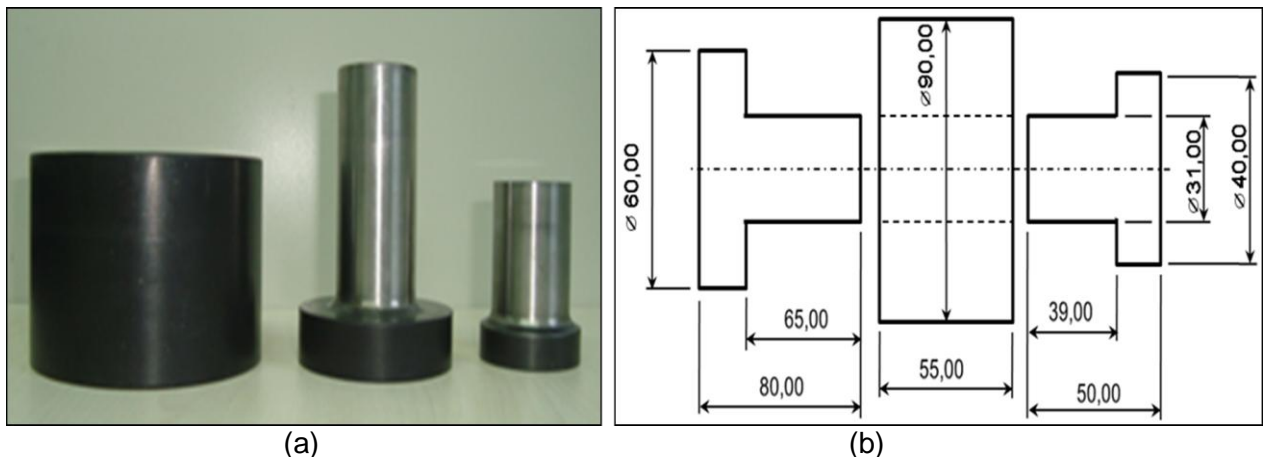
(a) Matriz utilizada para compactação do cilindro para usinagem do estator do mini – motor (b) dimensões da matriz
